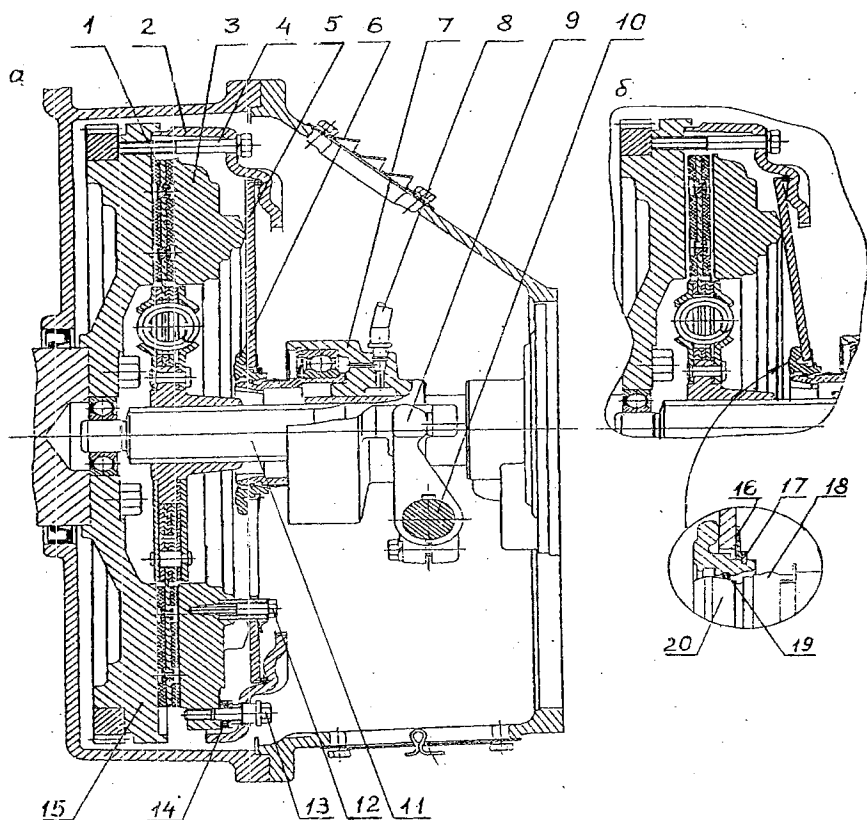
Сцепление однодисковое с тарельчатой пружиной вытяжного типа:
